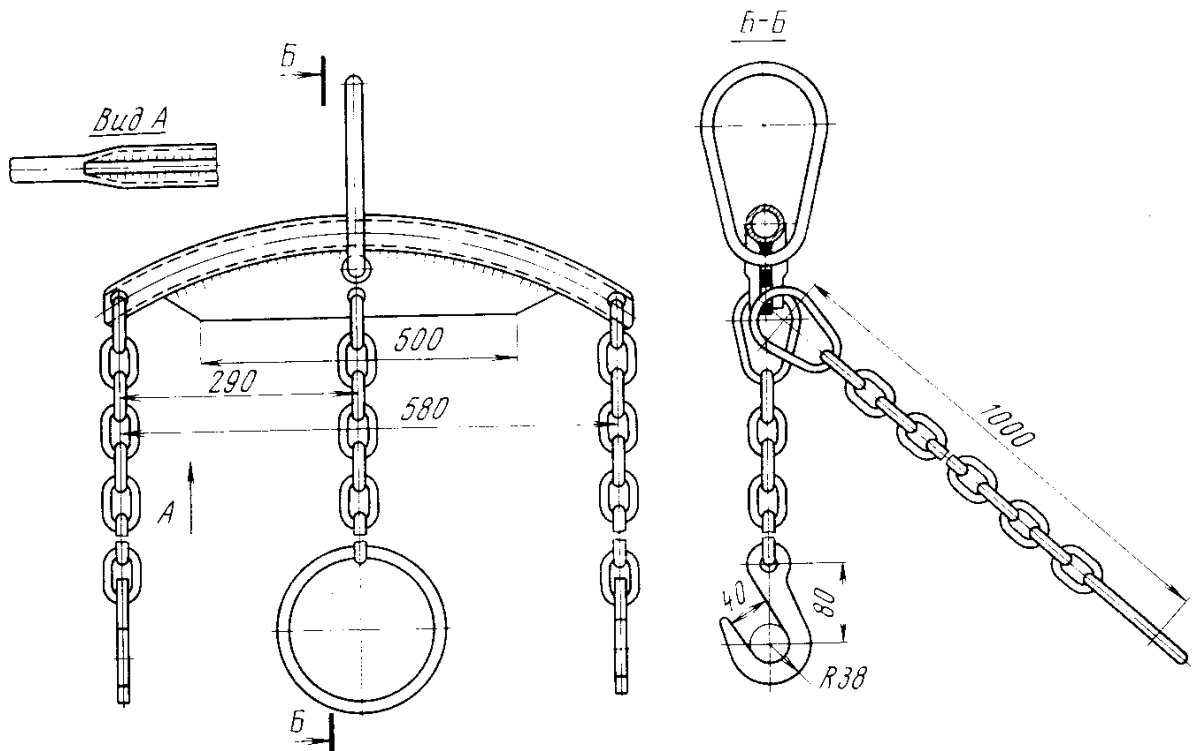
Приспособление для подвески силового агрегата к подъемному устройству
